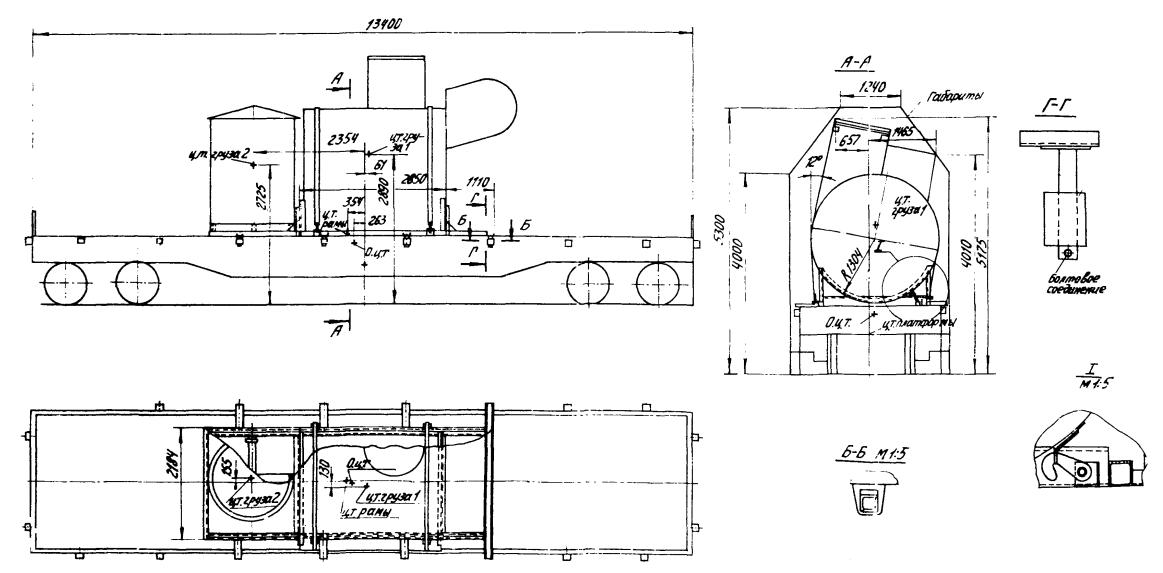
Схема крепления ИСУ БУП связи на железнодовожной платформе Р = 62 т
